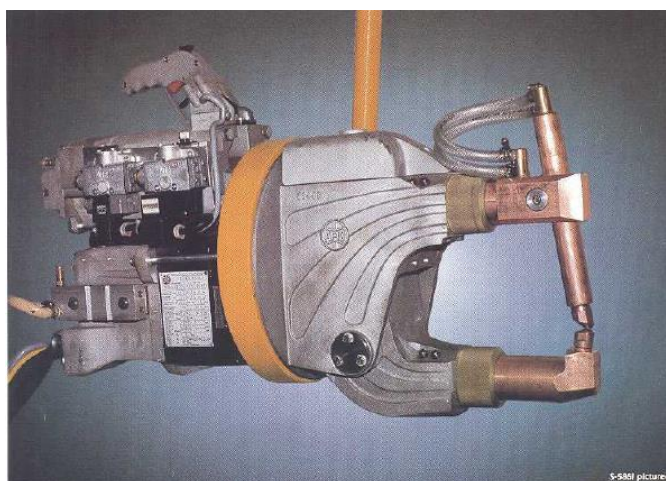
Клещи сварочные S 5861
